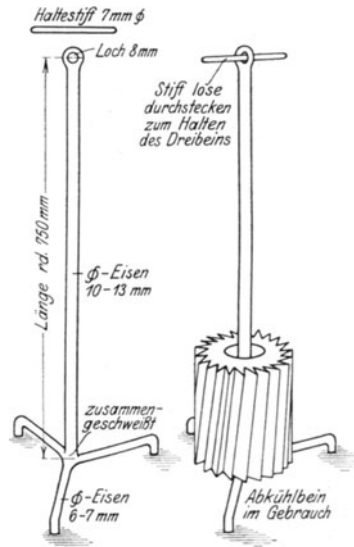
Dreibein zum Abkühlen von Fräsern.
